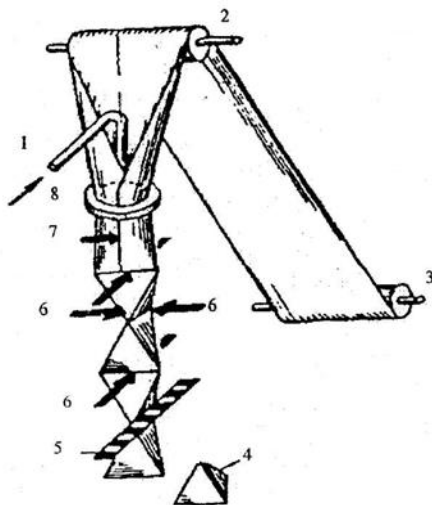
Схема утворення пакетів з молоком на автоматах типу "Тетра Пак": 1 – трубопровід подачі молока; 2 – верхній напрямний ролик; 3 – рулон стрічки пакувального паперу; 4 – пакет з молоком; 5 – пристрій для
